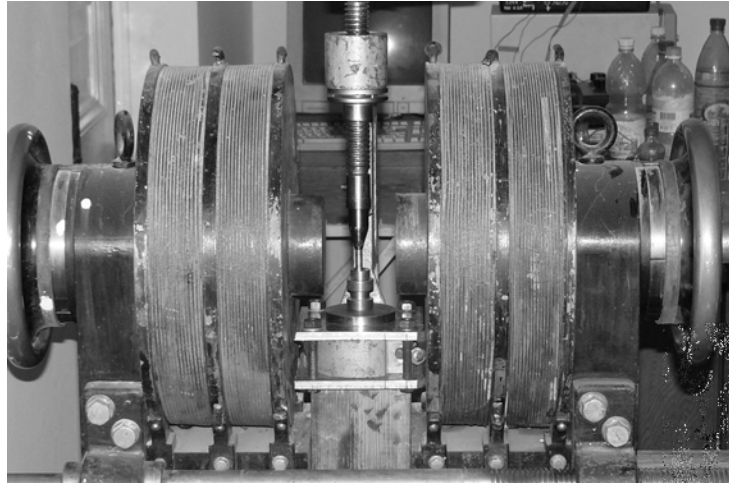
Установка для штамповки заготовок с применением внешнего магнитного поля
